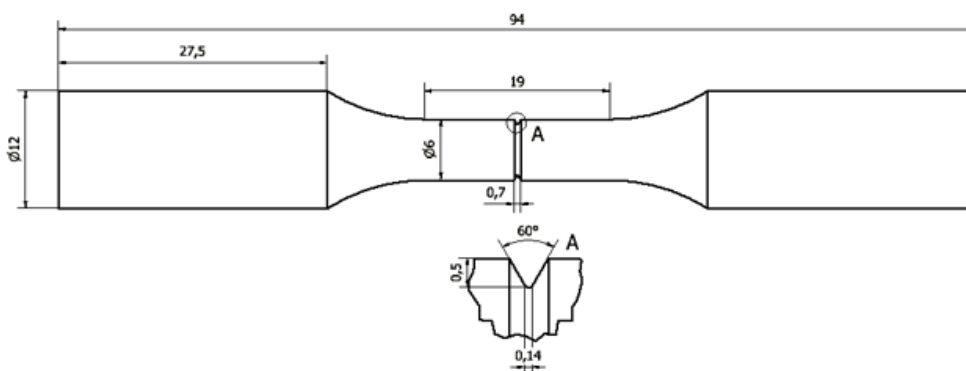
Geometria dos provetes, com entalhe com forma em "V", dimensões em milímetros.
